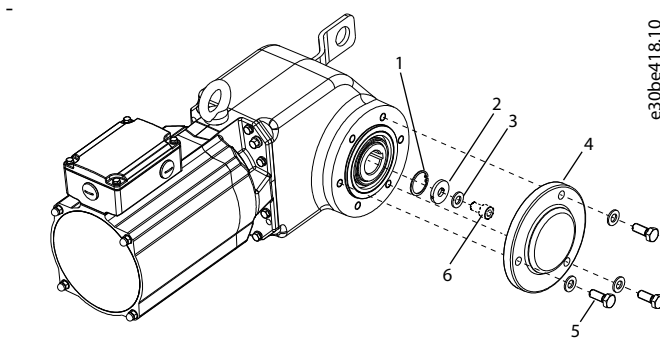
Conjunto de la disposición de montaje y la cubierta del eje hueco
